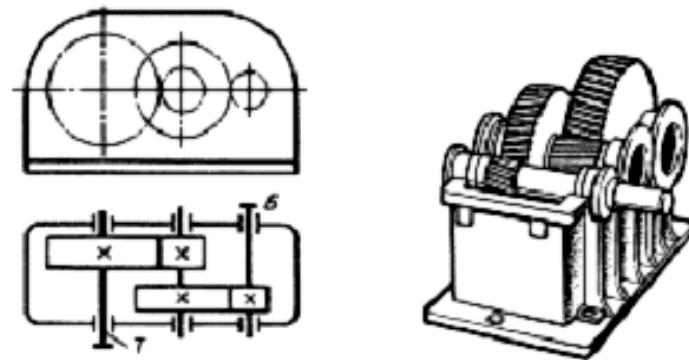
Двухступенчатый цилиндрический редуктор горизонтальный
